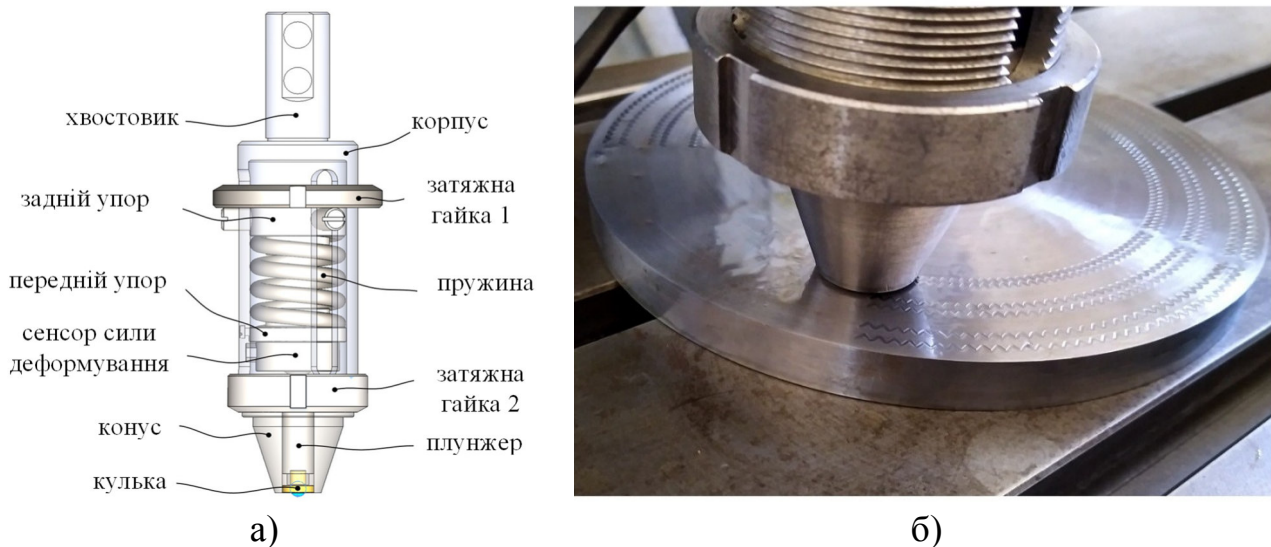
Схема інструменту та встановлення його на фрезерному 5-ти координатному верстаті для формування ЧРМ на торцевих поверхнях тіл обертання:
